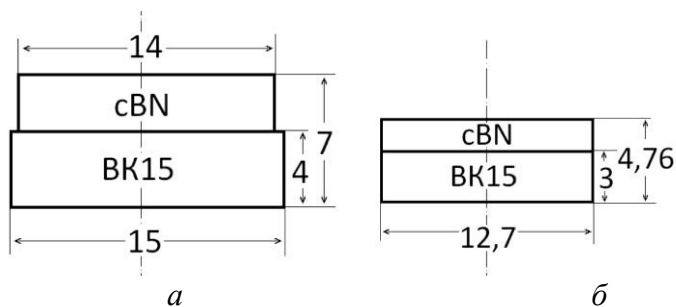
Форма і розміри спеченої заготовки (а) і ріжучої пластини (б) двошарового $PCBN$ композиту
